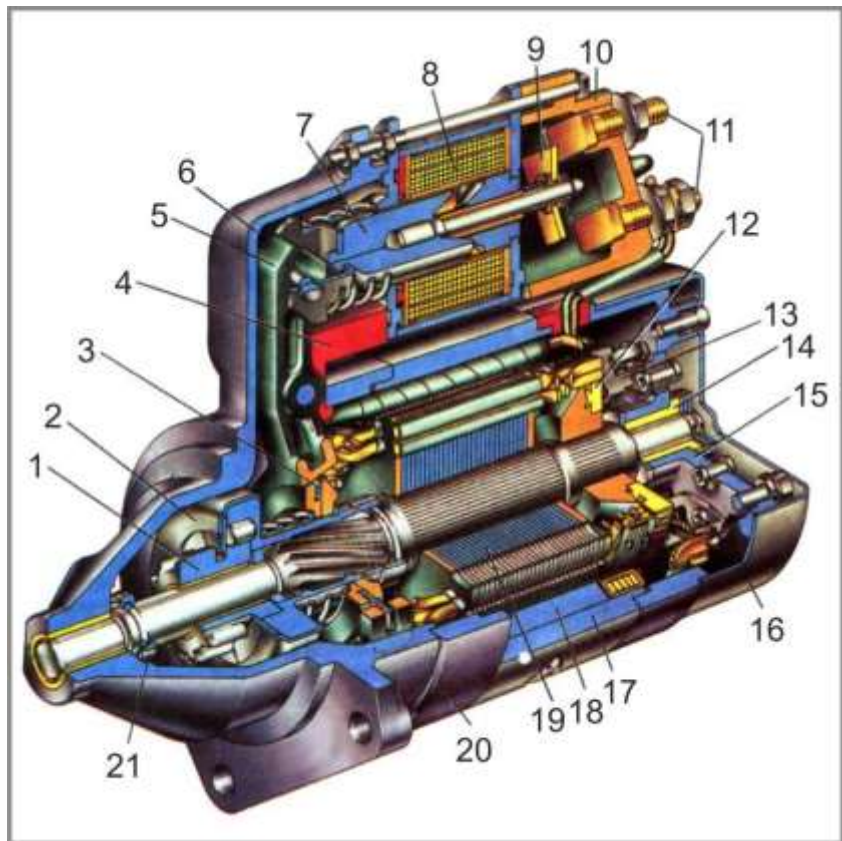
Будова стартера: 1 – шестерня привода; 2 – обгінна муфта; 3 – повідкового кільце; 4 – заглушка; 5 – важіль привода; 6 – кришка; 7 – якор реле; 8 – обмотка реле; 9 – контактна пластина; 10 – кришка реле; 11 – контактні виводи; 12 – колектор; 13 – щіткотримач; 14 – втулка для якоря; 15 – кришка; 16 – кожух; 17 – корпус; 18 – полюс статора; 19 – якор; 20 – проміжне кільце; 21 – обмежувальне кільце
